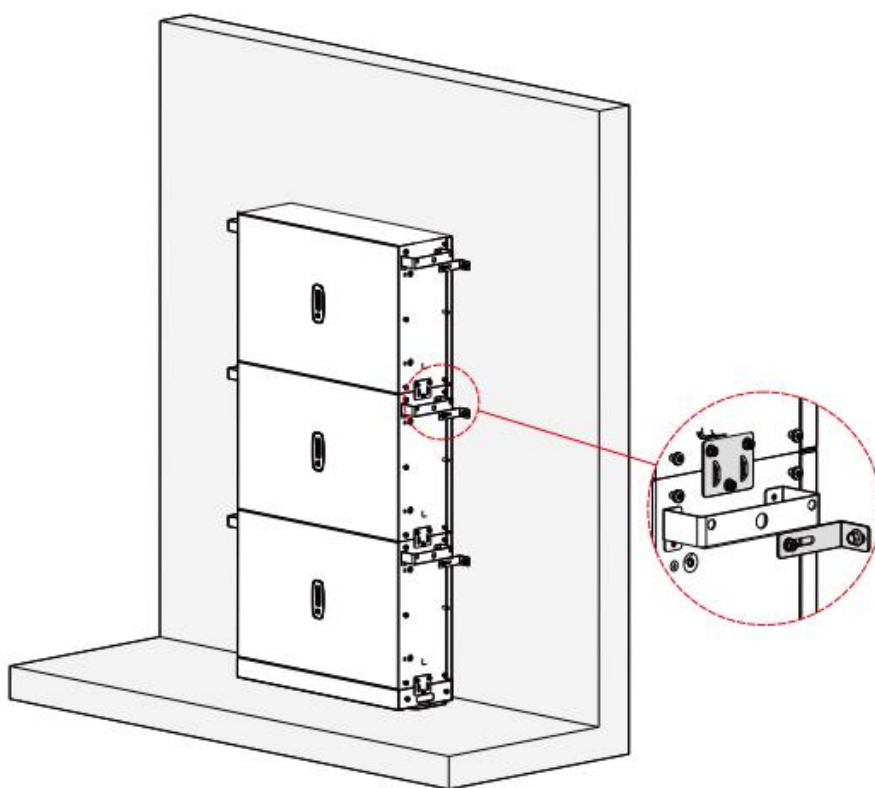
Collegamento della Staffa per Montaggio a Parete del Pacco Batteria
